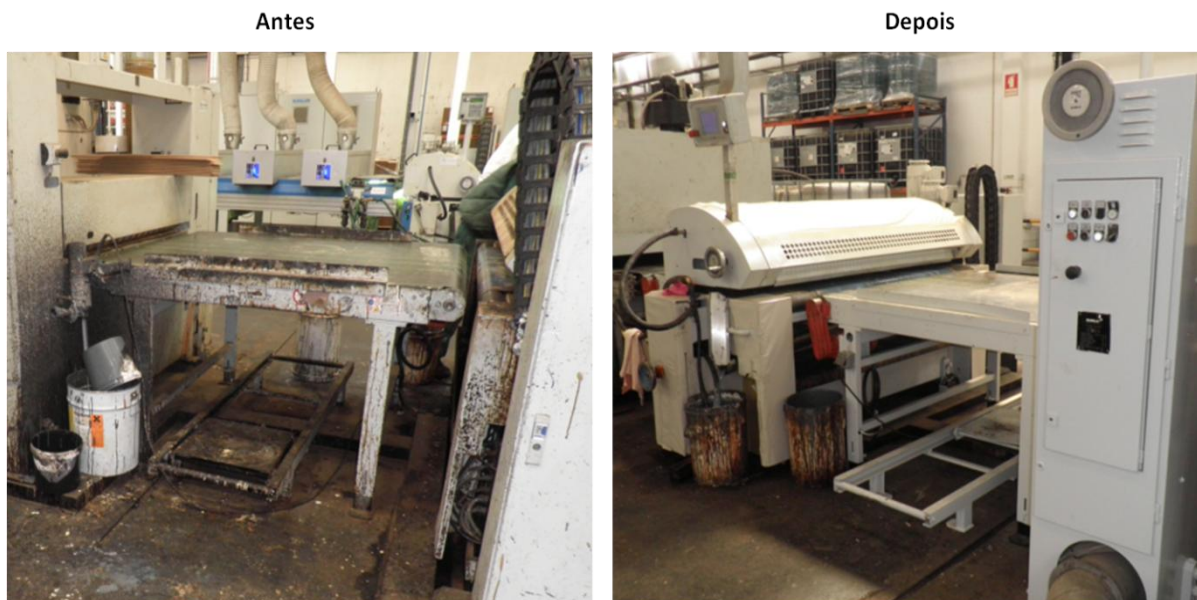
Pintura da máquina limpeza, transportador e máquina de pintura
